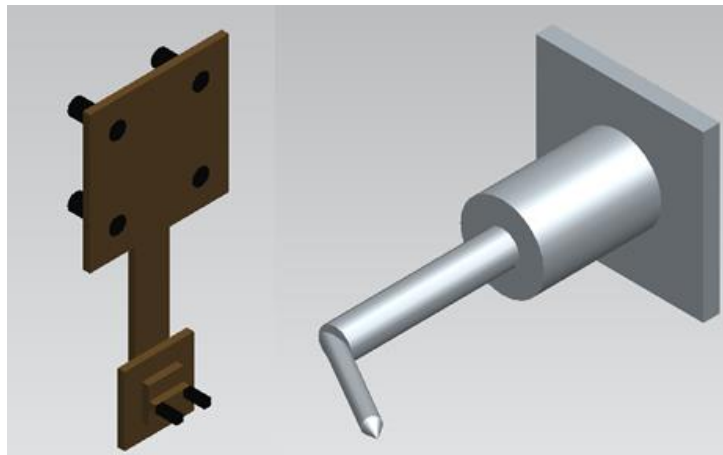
Herramienta doble de manipulación (izquierda) y boquilla de soldadura (derecha)
